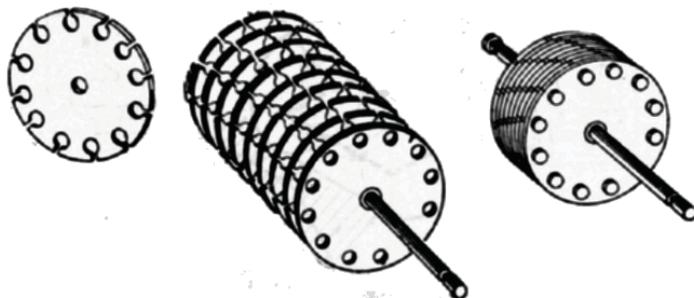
Il rotore è formato da un pacco di dischi.
